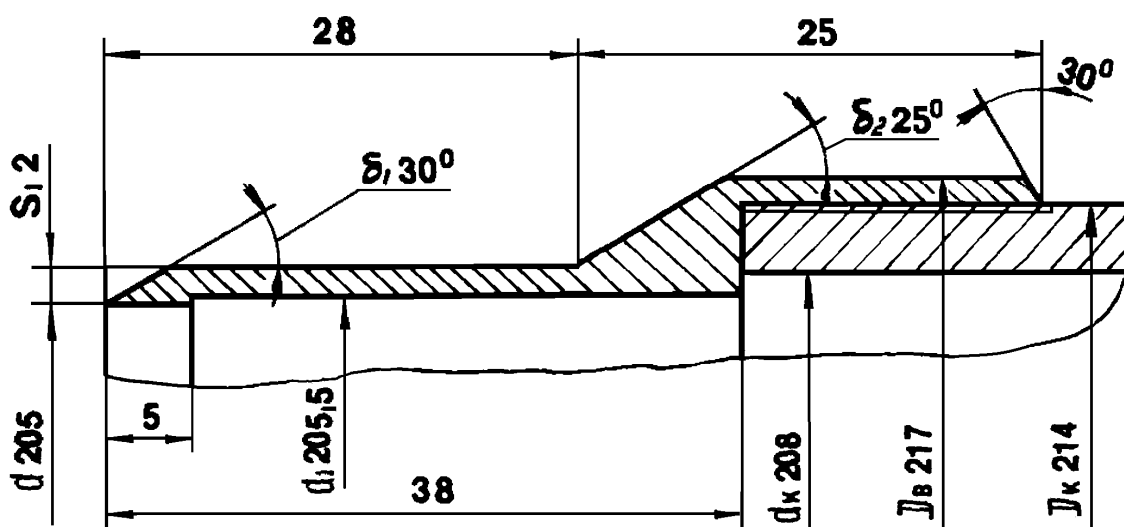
Конструкция башмака грунтоприёмной гильзы с двухступенчатой конусной наружной поверхностью
